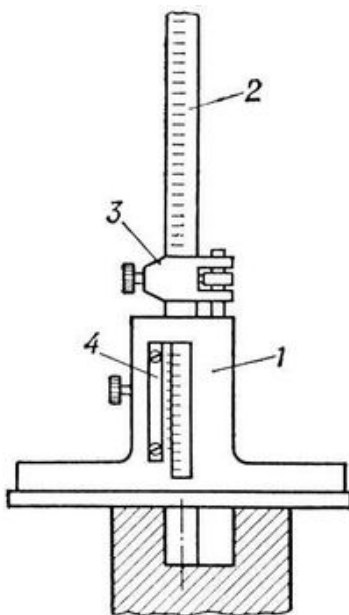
Конструкция штангенглубиномера: 1 – основание; 2 – штанга; 3 – микрометрическая подача; 4 – нониус
